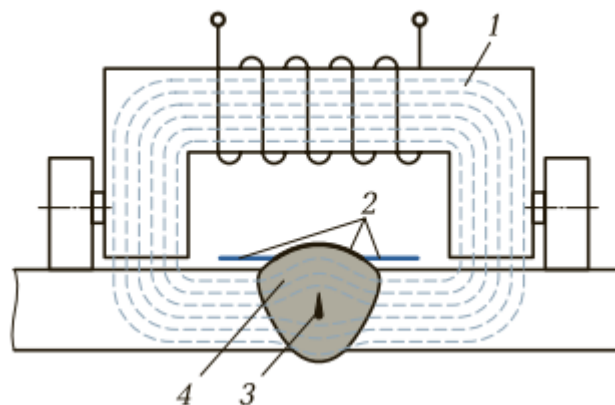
Схема магнитографического контроля: 1 — намагничивающее устройство; 2 — магнитная пленка; 3 — дефект; 4 — сварной шов
